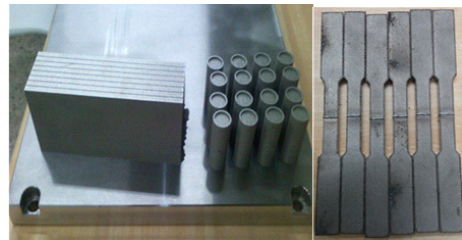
3D printed plate and brazing test piece(left) Electron beam welded test pieces(sub- ASTM E8)(우)
